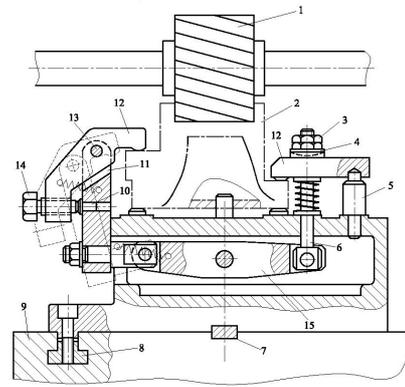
Fräsvorrichtung für Gussgehäuse
